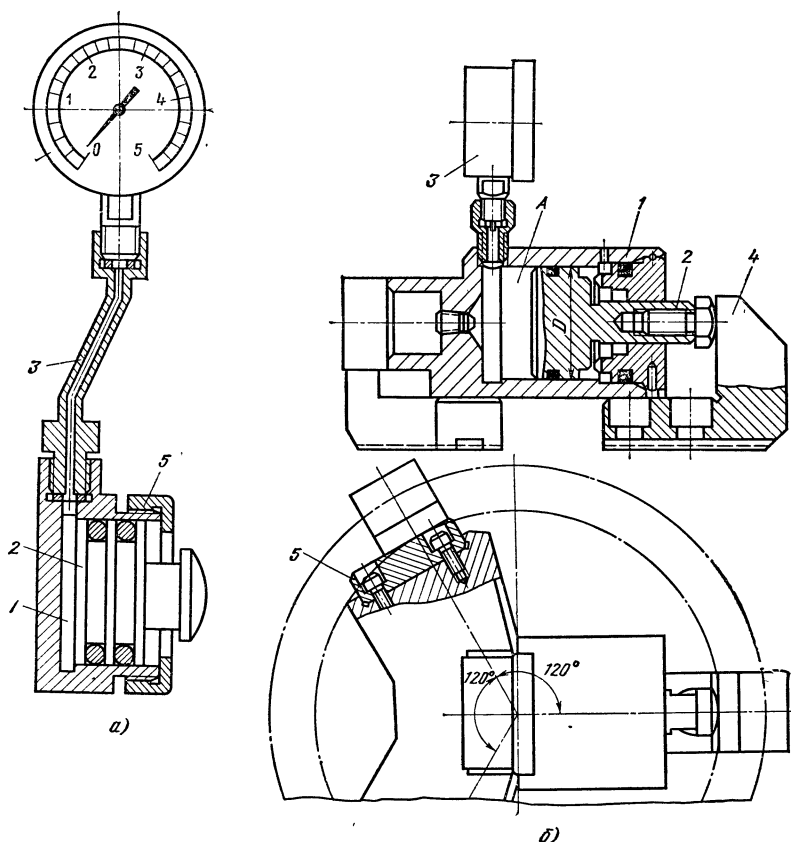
Гидравлический динамометр для контроля усилия зажима в приспособлении:
